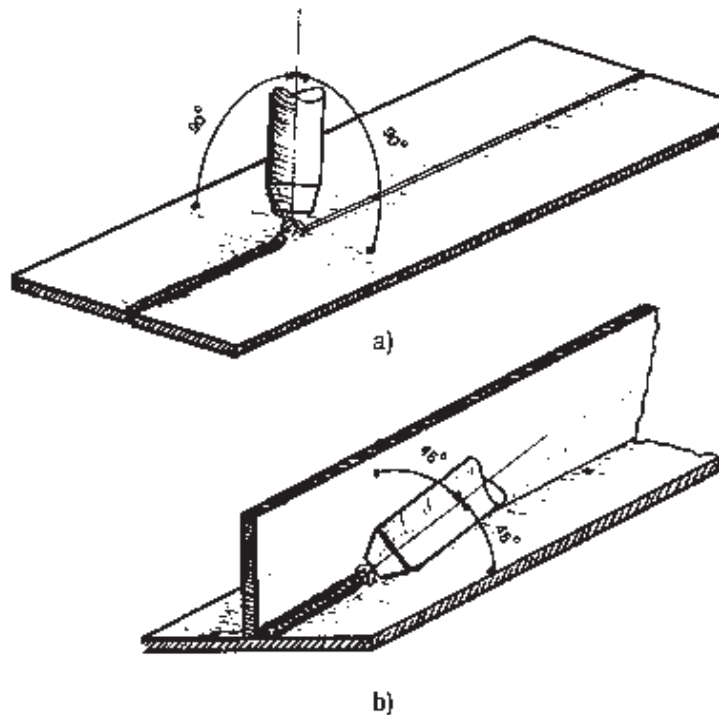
Muestra los ángulos de trabajo para dos tipos de soldaduras, a) Soldadura a tope, b) Soldadura de filete.
